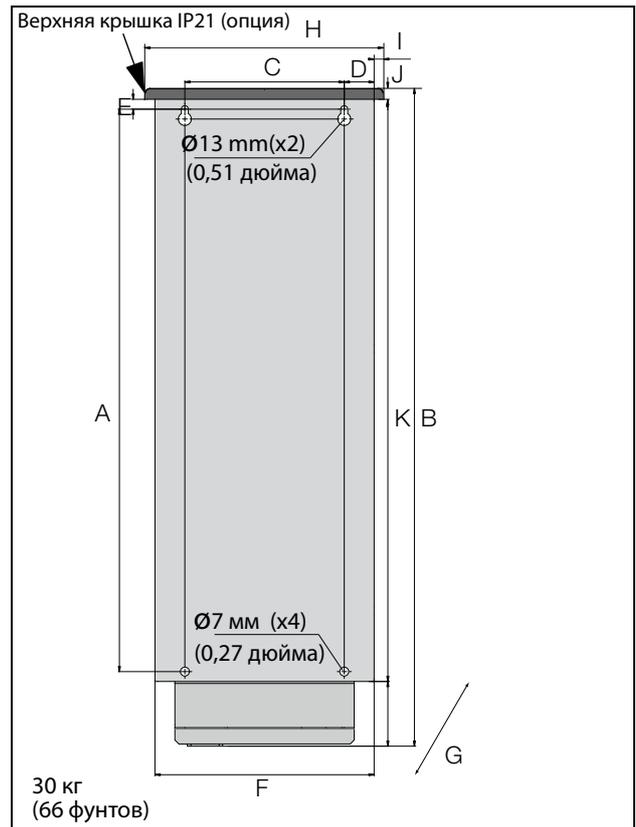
Устройство Emotron FDU моделей с 48-072 по 48-105 (размер корпуса D2), моделей с 69-033 по 69-058 (размер корпуса D2(69)), вид сзади.
